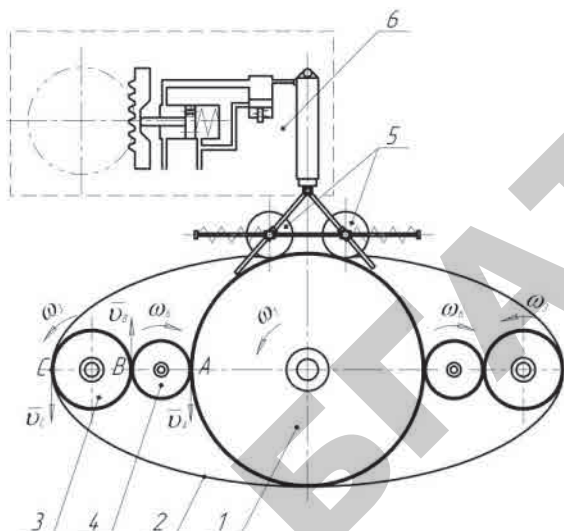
Колесо-гусеничный движитель: 1 – ведущее колесо; 2 – гибкий обод; 3 – ведомый ролик; 4 – промежуточный ролик; 5 – обжимные катки; 6 – гидросистема
